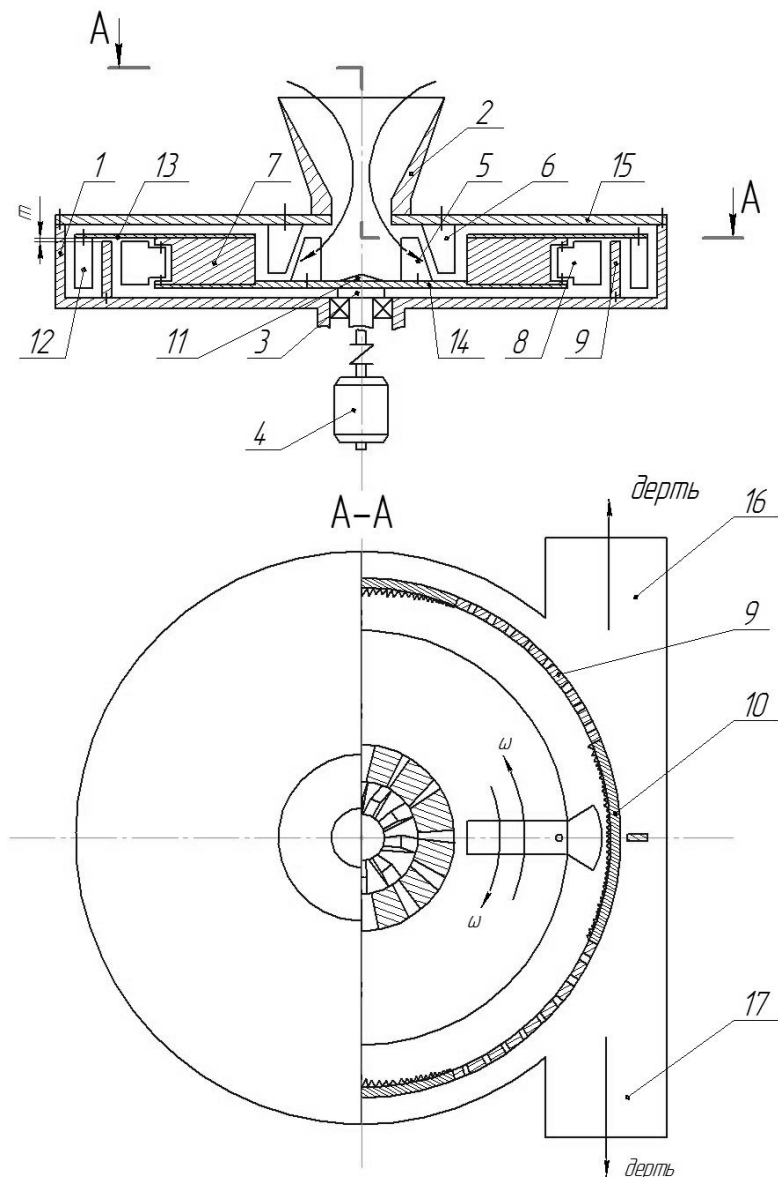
Функциональная схема двухступенчатой роторно-молотковой дробилки: 1 – корпус; 2 – загрузочный бункер; 3 – ротор; 4 – привод; 5 – нижний кольцевой выступ; 6 – верхний кольцевой выступ; 7 – разгонные лопасти; 8 – молотки; 9 – решетка; 10 – рифленые деки; 11 – распределительный конус; 12 – выбросные лопасти; 13 – верхний диск; 14 – нижний диск; 15 – крышка, 16, 17 – выбросные патрубки
